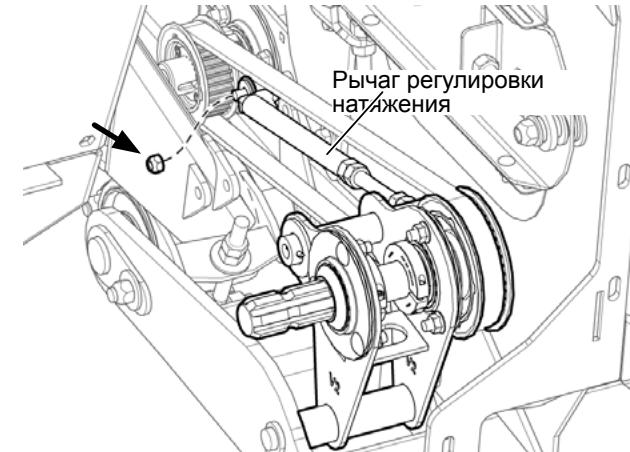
Отсоединение рычага регулировки натяжения от подрамника
